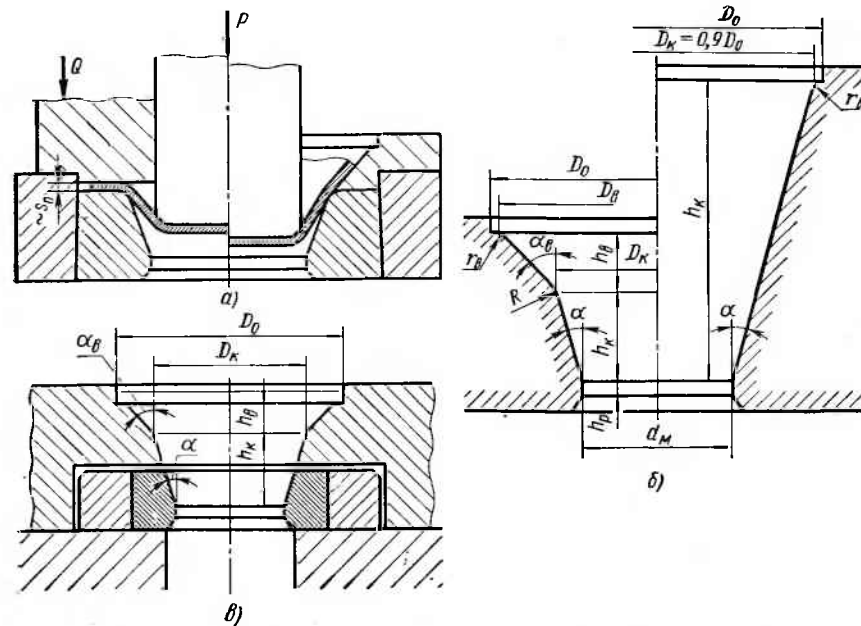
Варианты двухконусной матрицы с расчетными параметрами: а — в универсальном штампе (справа — составной двухконусный профиль для вытяжки толстых заготовок, слева — одноконусный профиль для вытяжки тонких заготовок со складкодержателем); б — монолитное исполнение в сравнении с одноконусной матрицей для вытяжки толстых заготовок; в — с твердосплавной рабочей частью
